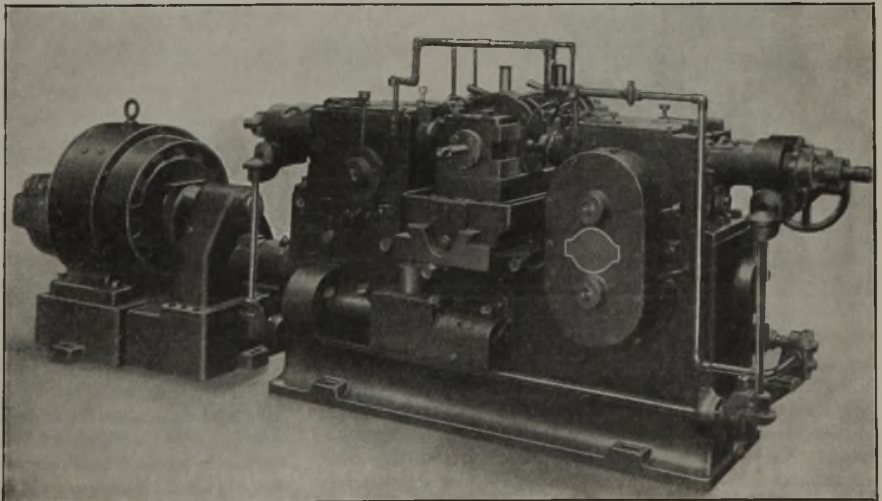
Rückansicht der Vierfach-Rippenplatten-Fräsmaschine.
